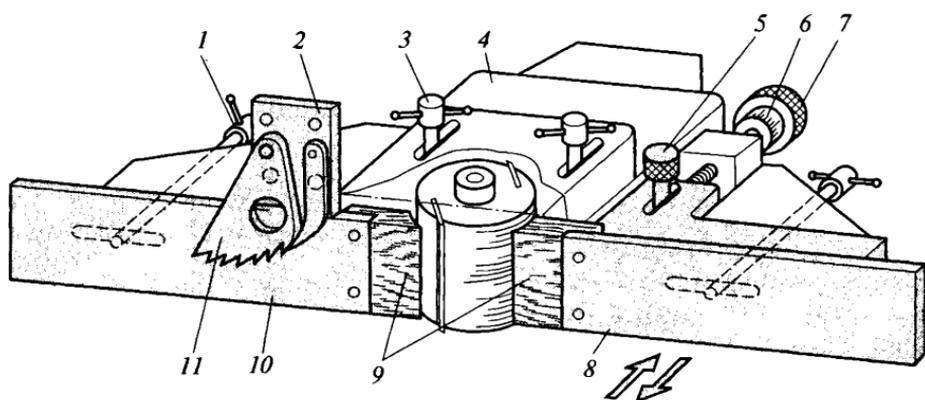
Настройка направляющих линеек фрезерного станка:
